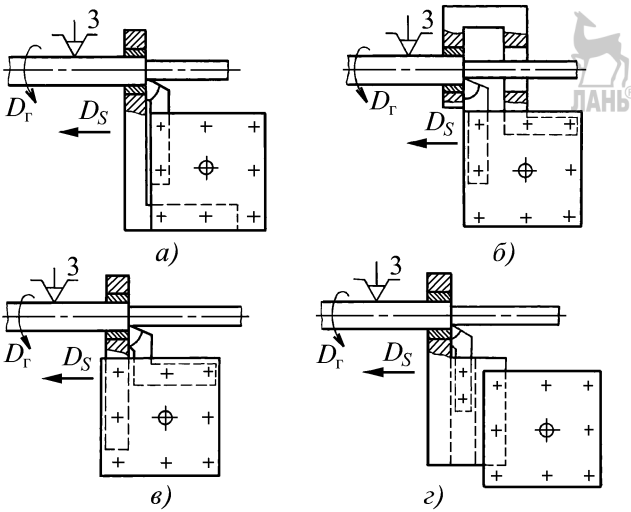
Способы крепления длинных валов с помощью планок с люнетными втулками:
